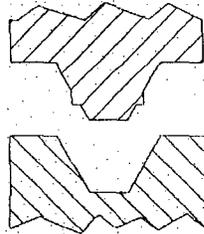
União chanfrada para soldagem ultrasônica.
